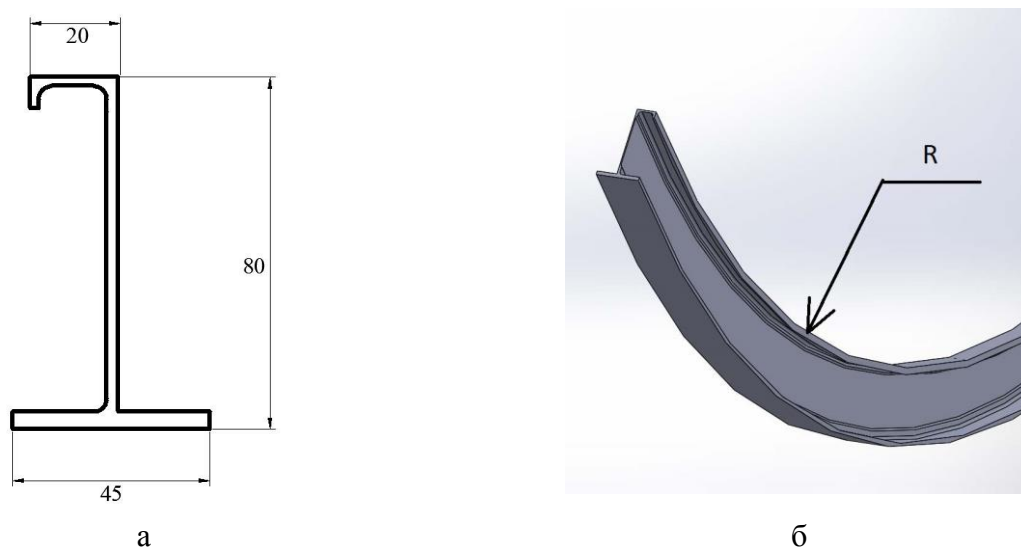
Пример сечения профиля заготовки шпангоута самолета: а – профиль пресованный или фрезерованный, б – общий вид профиля с продольным радиусом R
